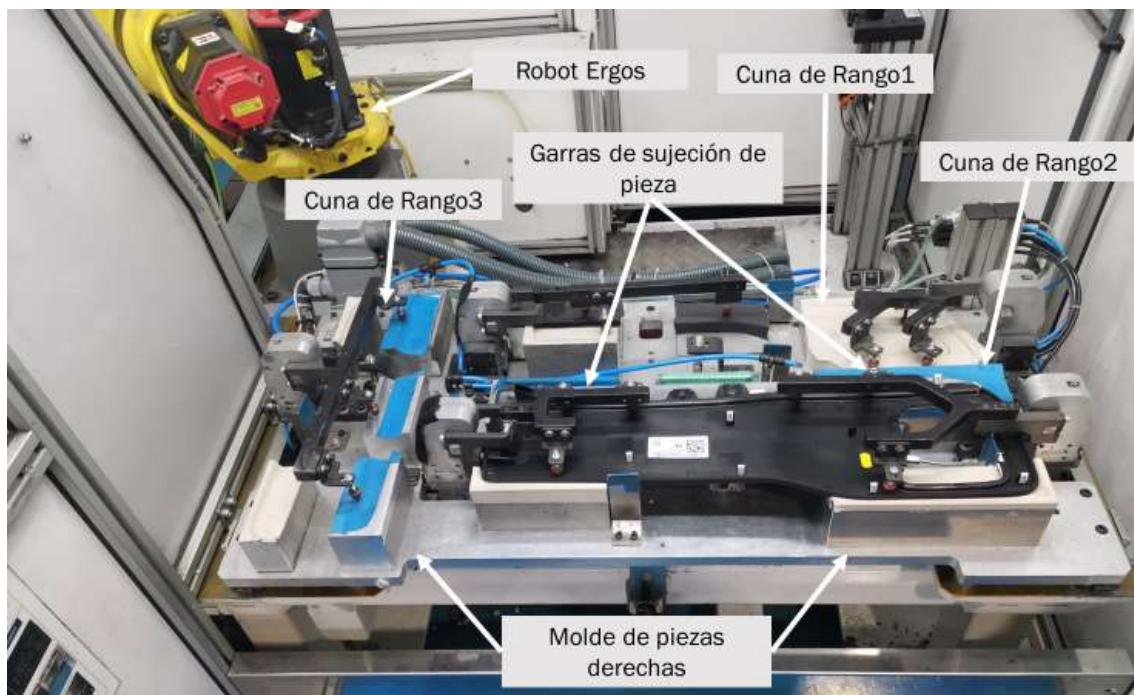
Cavidad derecha del robot Ergos con el molde de piezas derechas durante la soldadura de un medallón Rg2. Fuente: Elaboración propia
